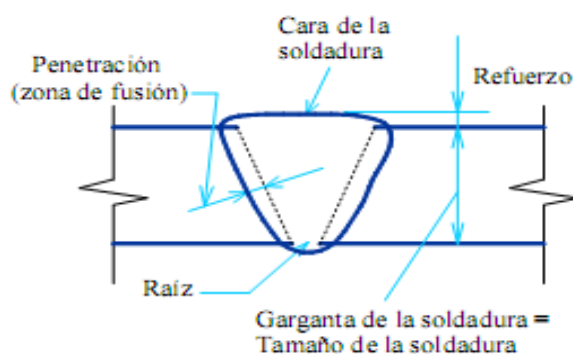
Preparación de la unión para la soldadura.
